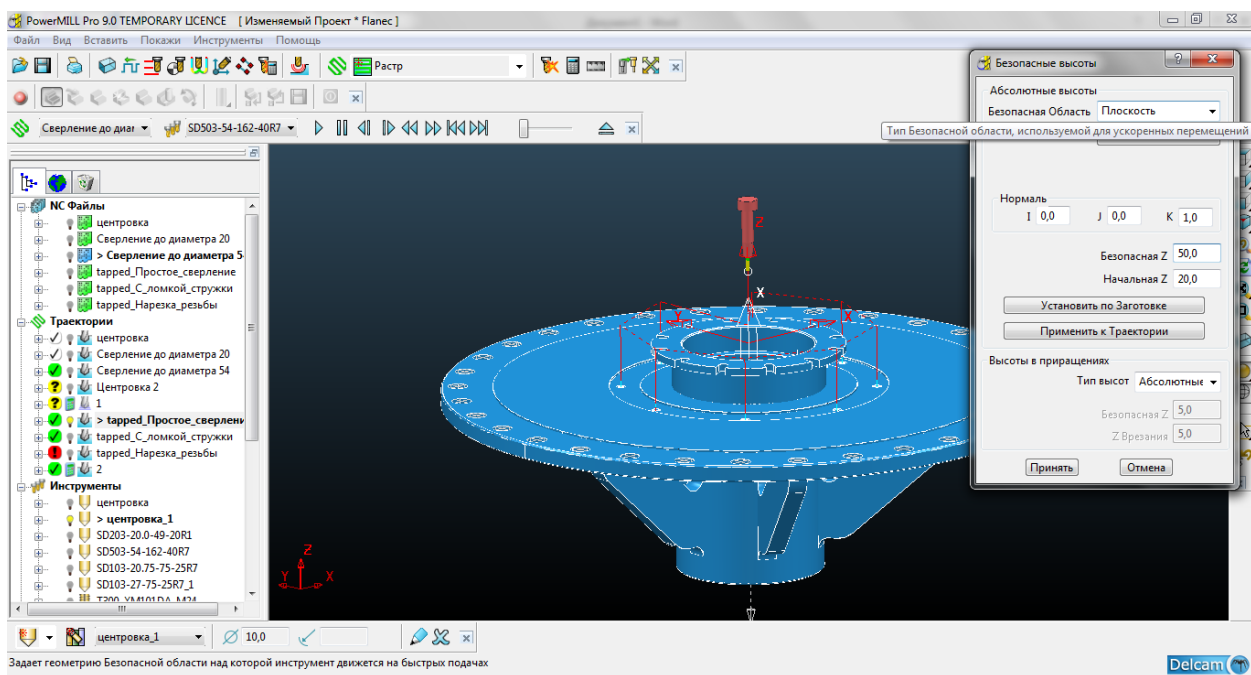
Вибір інструменту для обробки 8 отв М24
